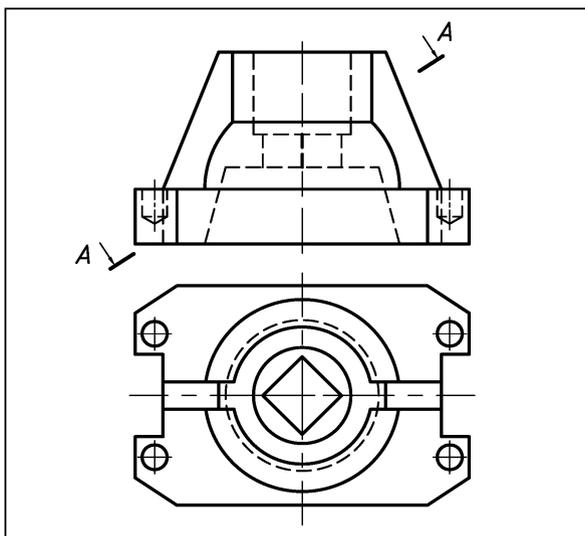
Вариант исходной заготовки чертежа детали с двумя плоскостями симметрии для выполнения простых разрезов
